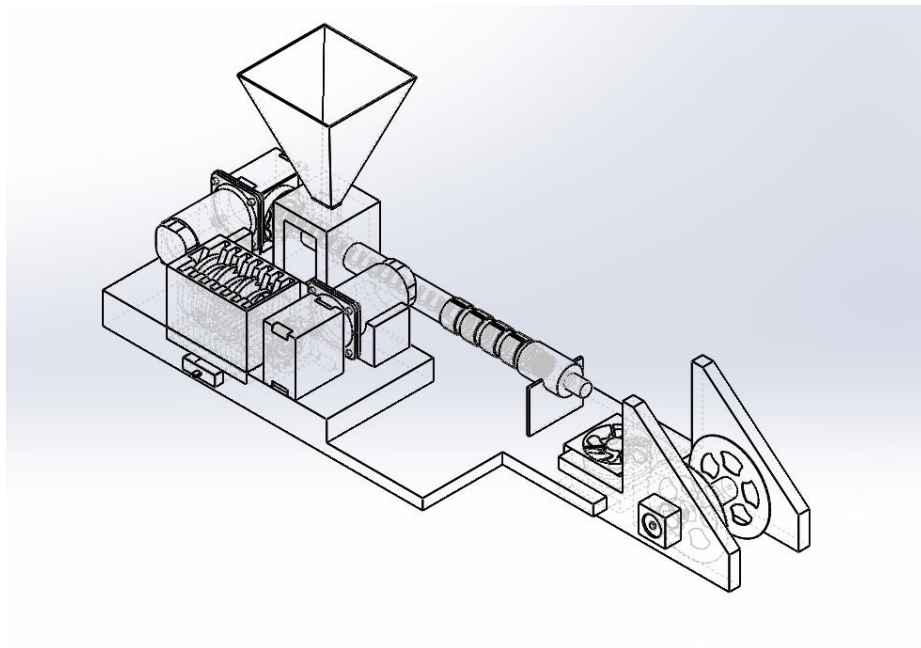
Ensamblaje final de la máquina extrusora vista 4
